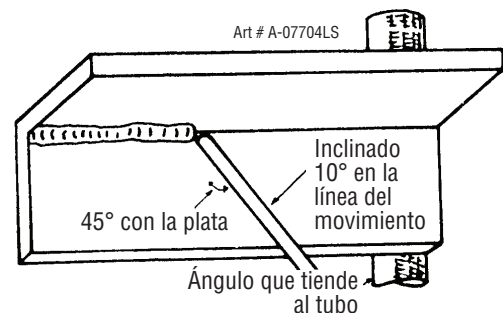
Soldadura de perfil en ángulo de posición en elevación
